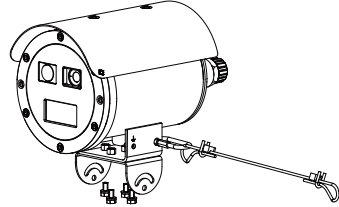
Instalarea părții superioare a articulației PT cu camera
